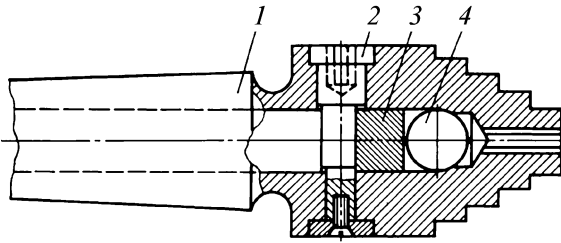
Многоступенчатая оправка для обработки колец и втулок
